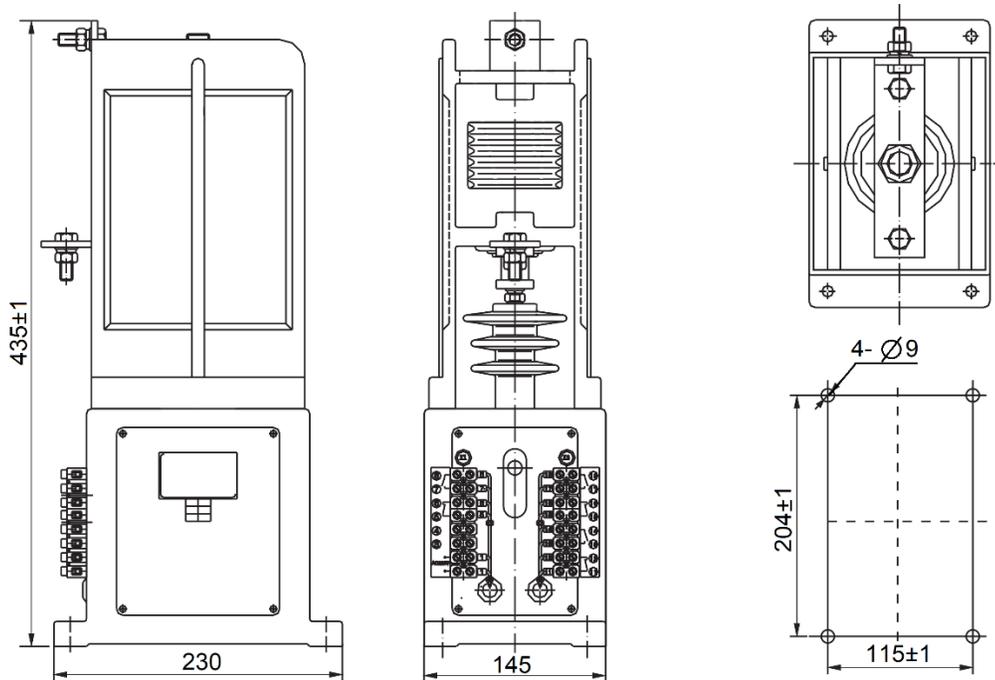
Габаритные размеры контакторов КВТ-6 на номинальные токи 160, 250, 400, 630 А одно полюсного исполнения и размеры монтажной площадки.
